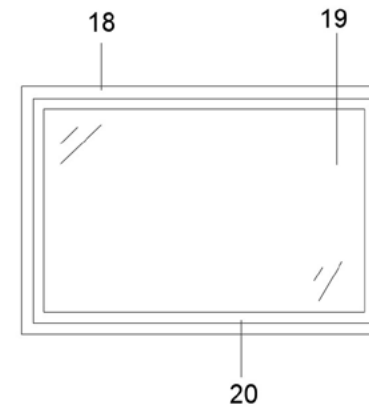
Detalle constructivo puerta de alacena HDPE reciclado con vidrio
